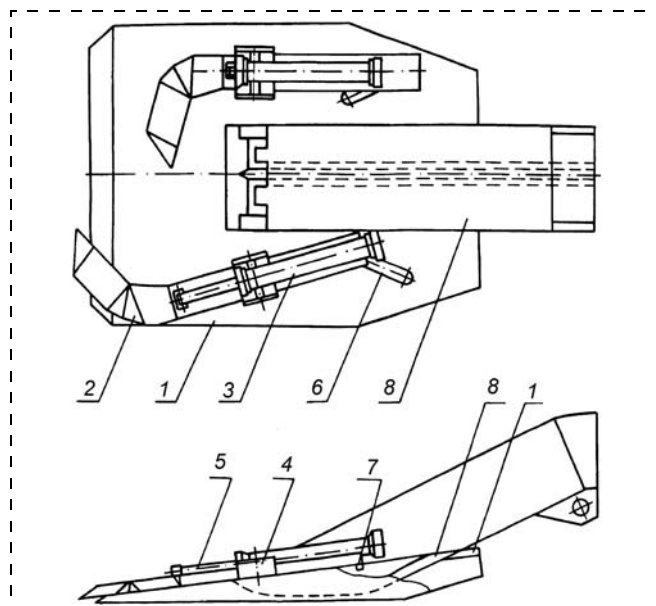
Погрузочный орган с клиновыми лапами, совершающими плоское движение: 1 — наклонный питатель; 2 — нагребавшие лапы; 3 — гидроцилиндр перемещения лапы; 4 — опора; 5 — шток гидроцилиндра; 6 — направляющий паз; 7 — палец с роликом; 8 — конвейер
